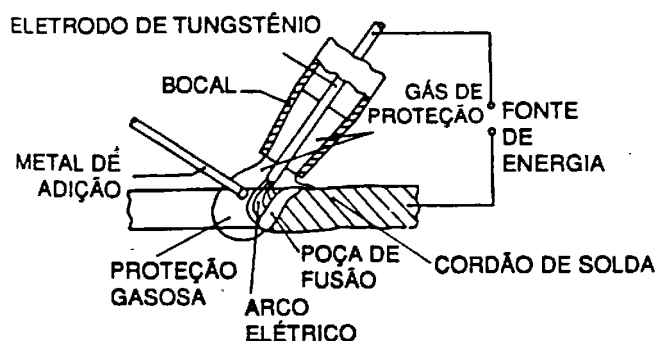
Processo de soldagem TIG⁽¹⁾
